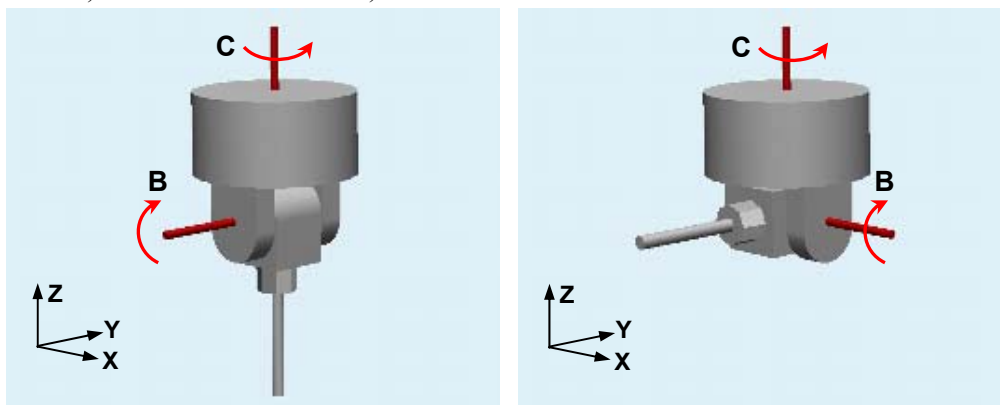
(а) Координаты положения рабочих органов станка B0 C0
